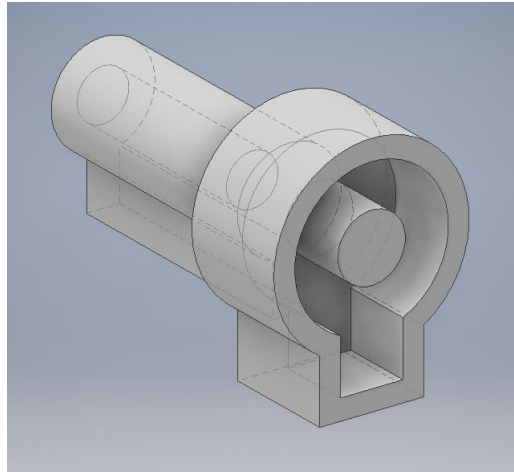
Acople diseñado para girar el rotor a partir del accionamiento del motor DC
